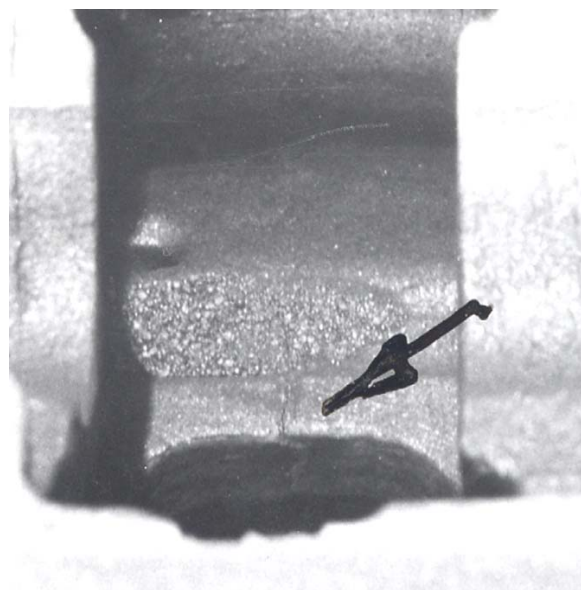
Фрагмент отливки «Блок цилиндров» с холодной трещиной
